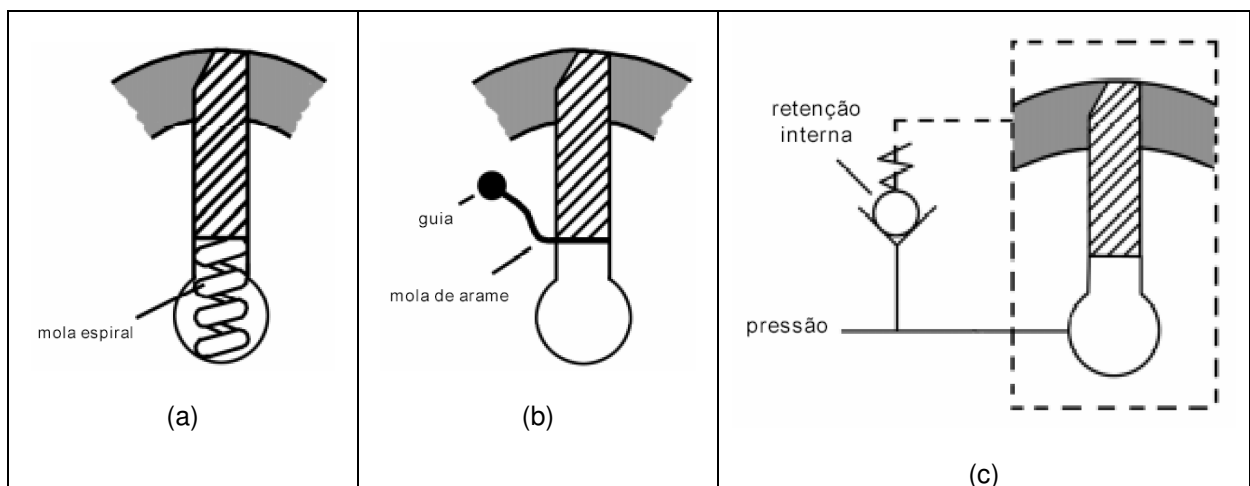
Exemplos de mecanismos para extensão das Palhetas do Motor
